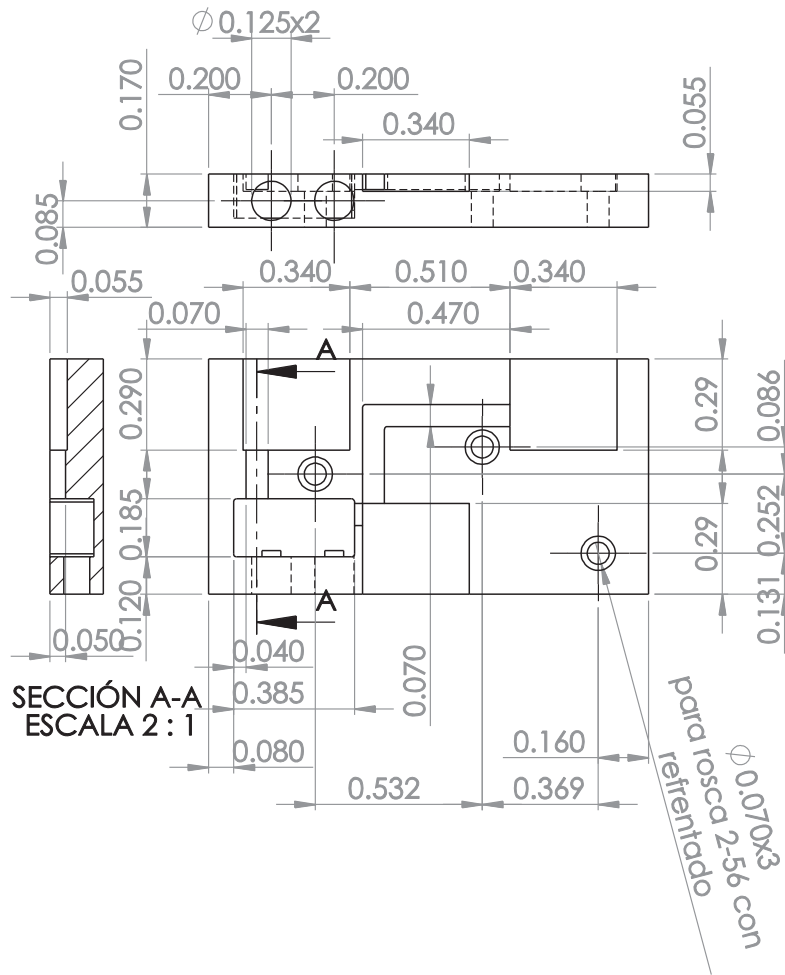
Dimensiones de la parte inferior de la montura lineal.
